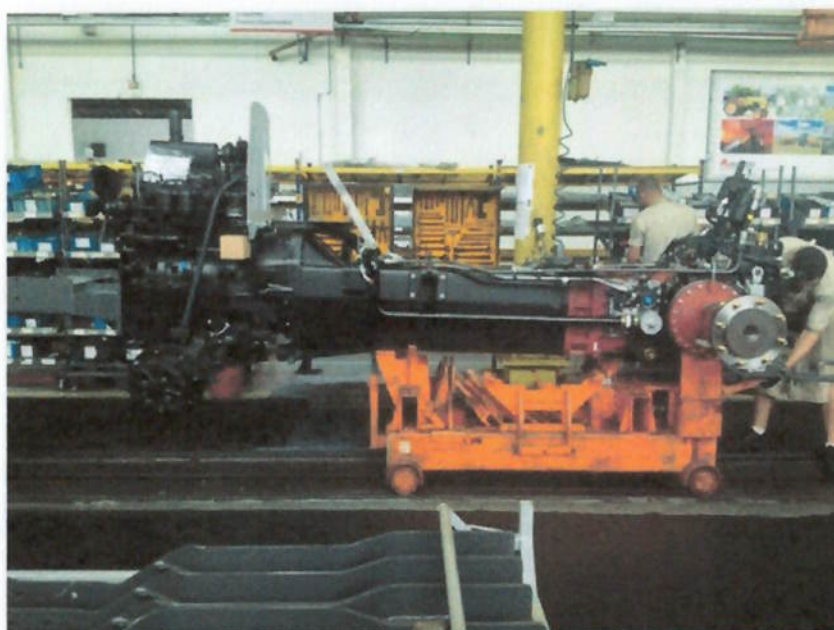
Da esquerda para a direita - Motor, Tanque e Transmissão: unidos, formam o Chassis
